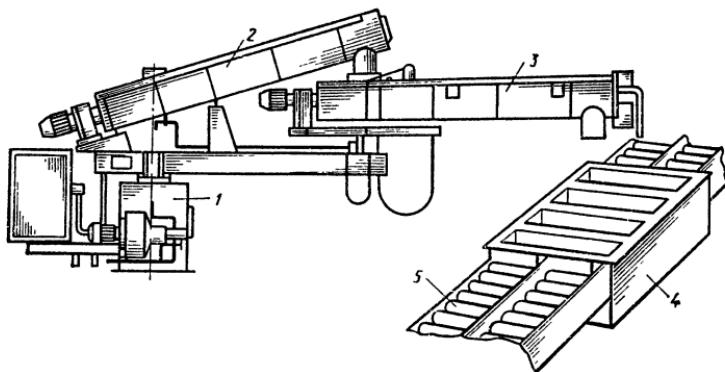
Смеситель непрерывного действия АМД-15 для приготовления быстротвердеющих смесей:
